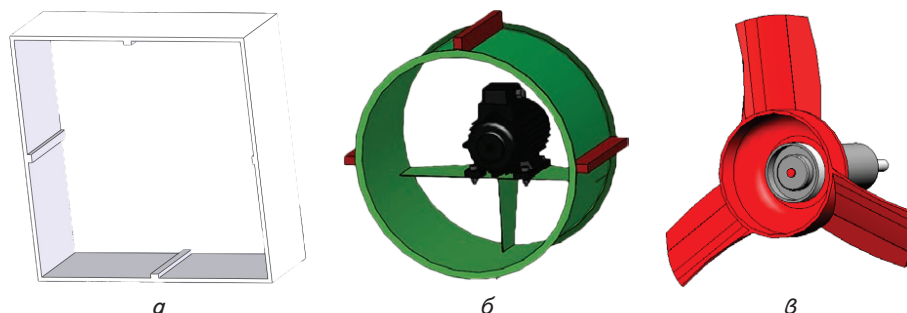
3D модель осевого вентилятора [6]: а – рама; б – защитный кожух с корпусом электродвигателя; в – ротор, крыльчатка и корпуса автобалансиров в сборе (составной ротор)
